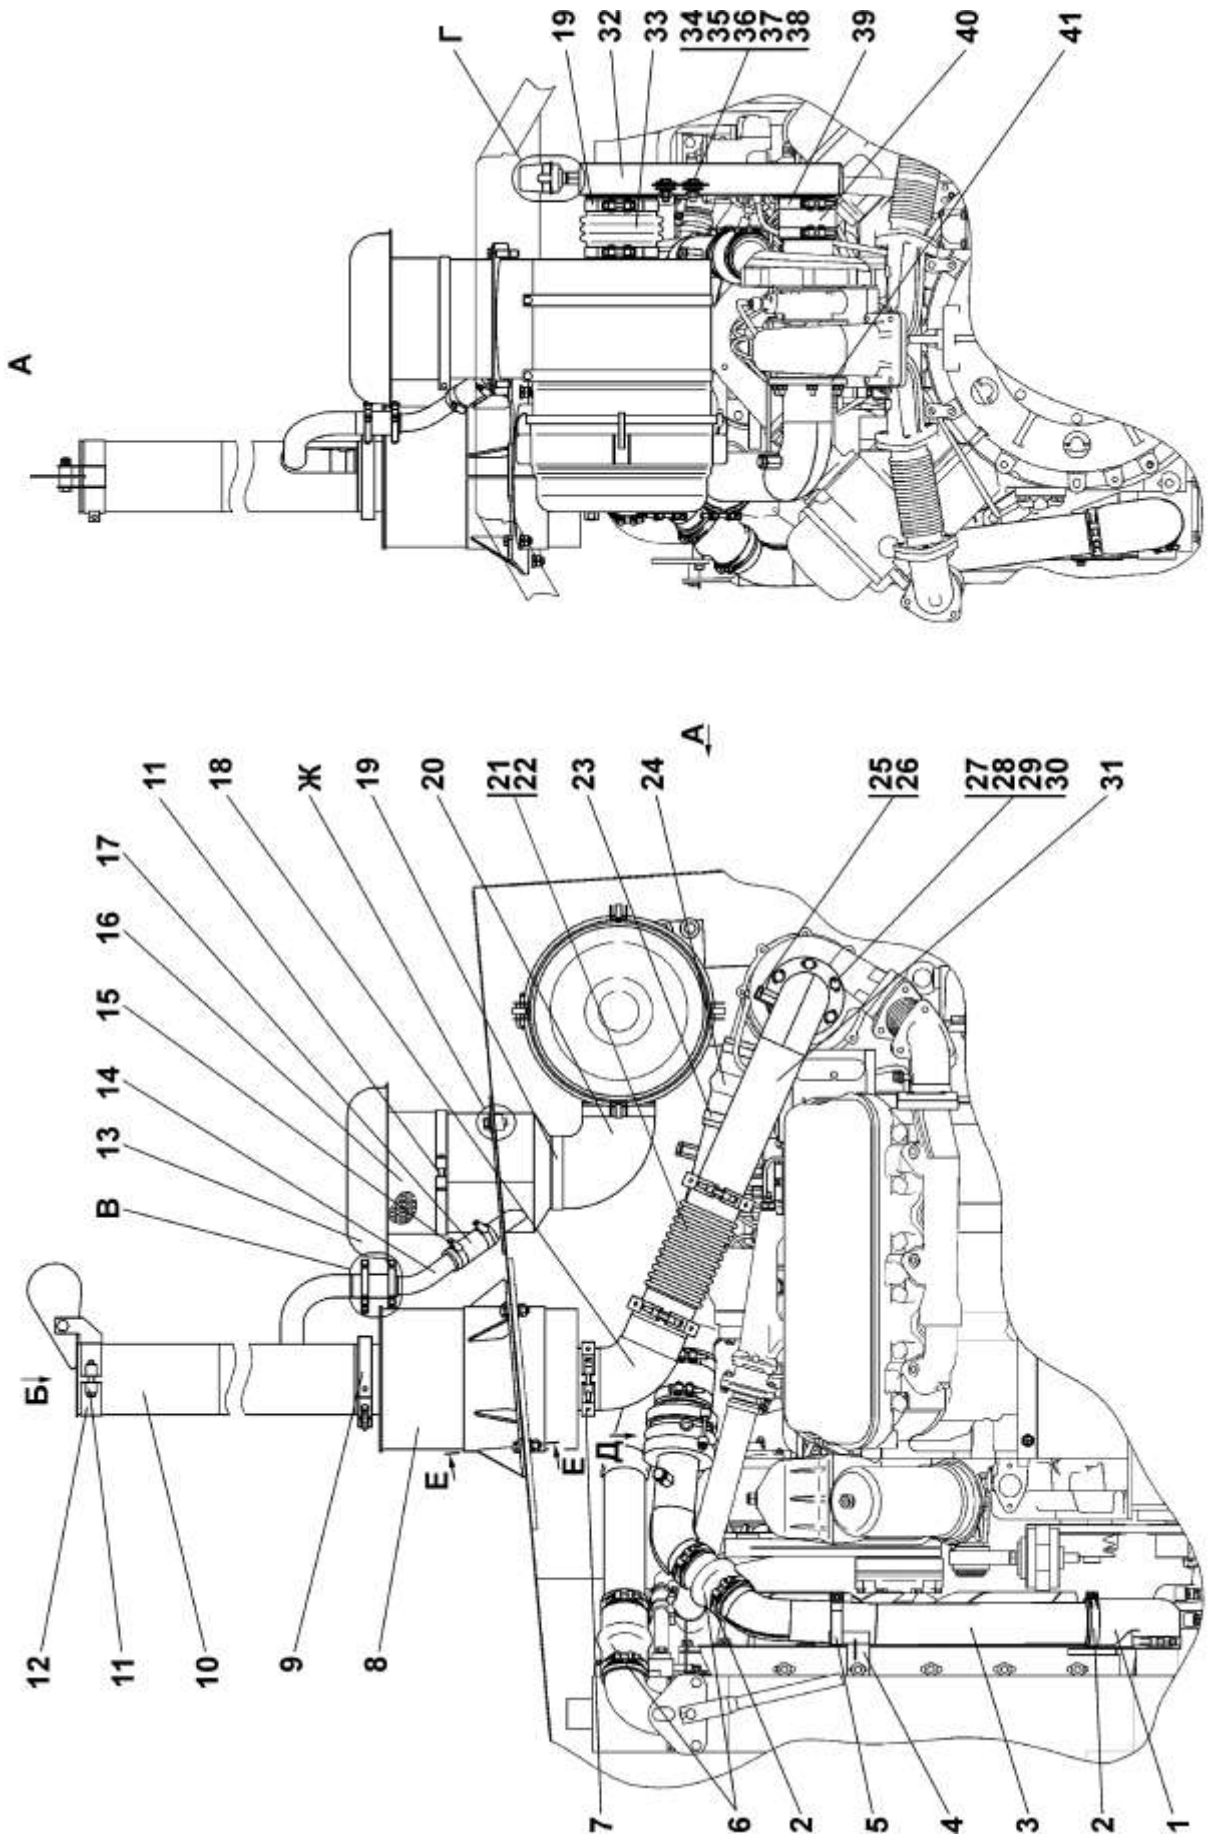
Установка системы воздухоочистки и выпуска
